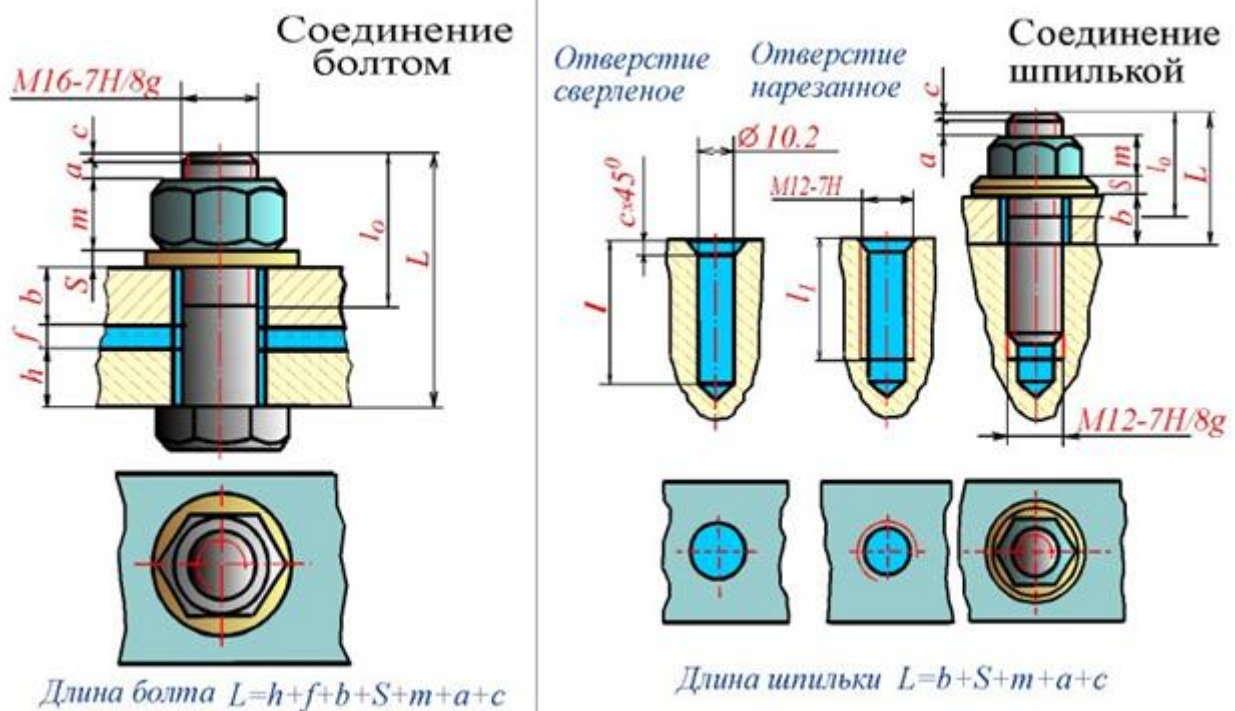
Изображение сборочного чертежа головки болтов и гайки
